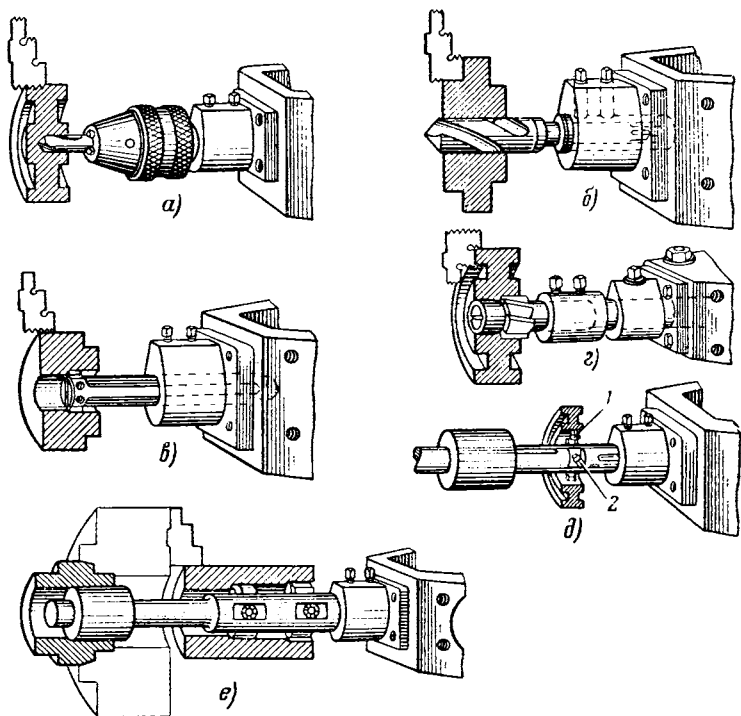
Приемы обработки отверстий на станках с вертикальным расположением оси револьверной головки
